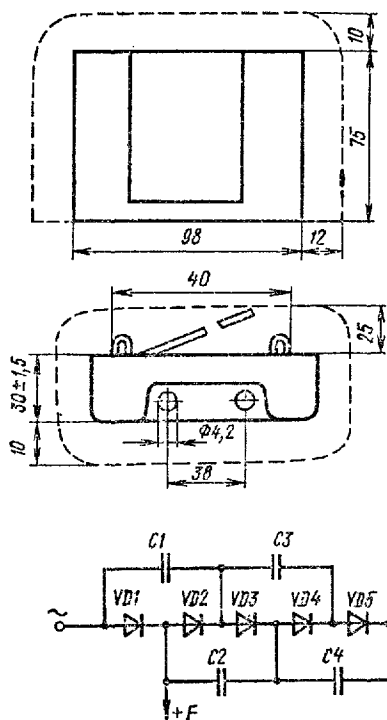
Общий вид, габаритные, присоединительные размеры и электрическая схема умножителя УН 3,5/25-1,2
